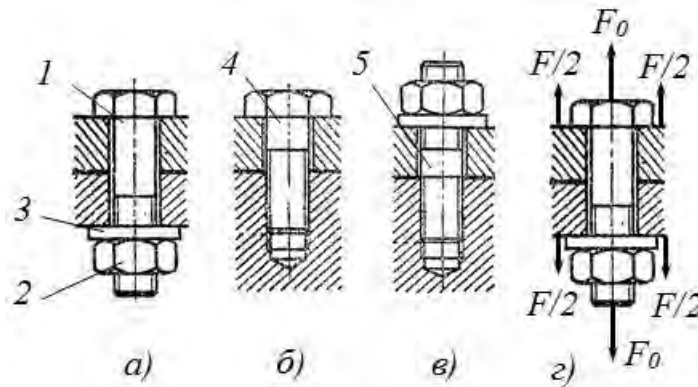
Види різьбових з'єднань: болтове (а), гвинтове (б), шпилькове (в) та розрахункова схема болтового з'єднання (г); 1 – болт; 2 – гайка; 3 – шайба; 4 – гвинт; 5 – шпилька.
